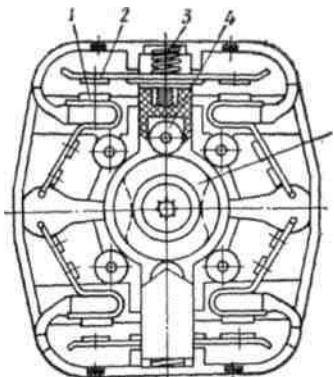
Пакет кулачкового вимикача: / — нерухомий контакт; 2 — контактний міст з рухомими контактами; 3 — пружина; 4 — ролик; 5 — кулачок
